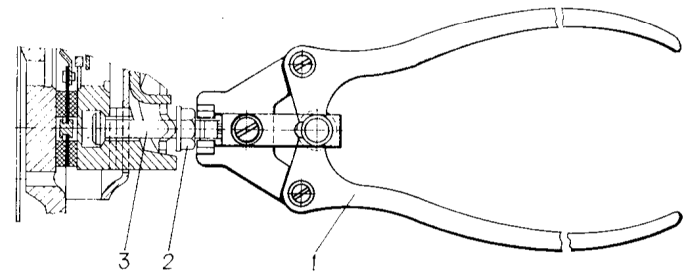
Клещи для фиксации регулировочных гаек пальцев сцепления:
